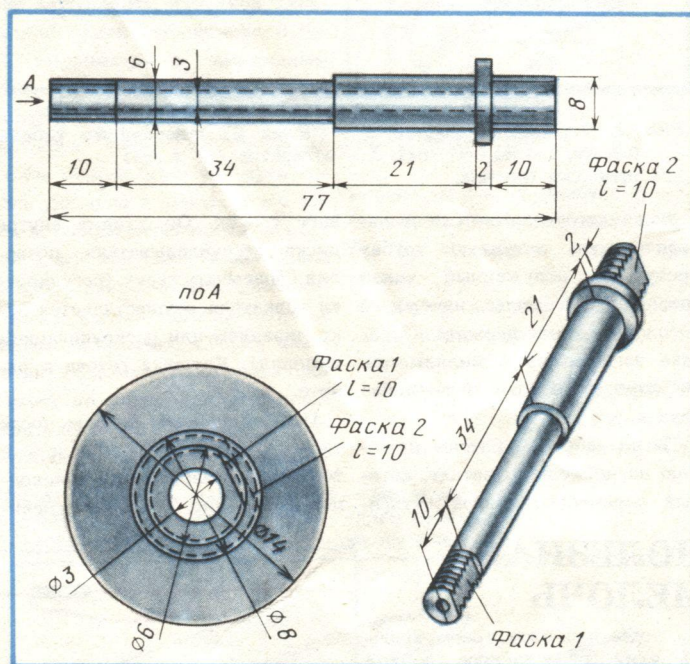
Изготовление дюралюминиевой оси малой конической шестерни.
